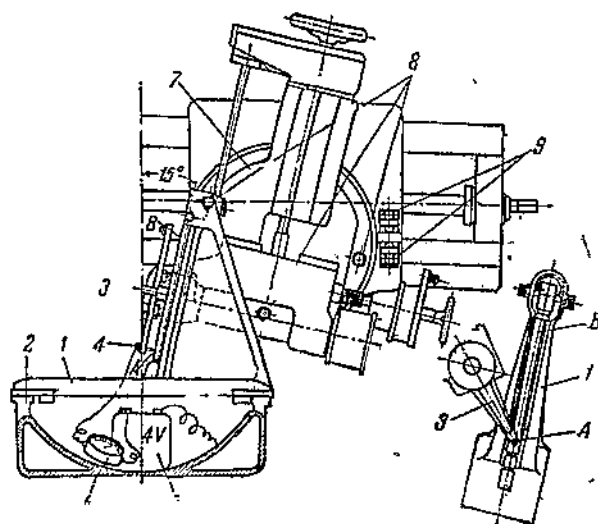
Приспособление для правильной установки шестерен и ведущих хомутиков на оправках.
